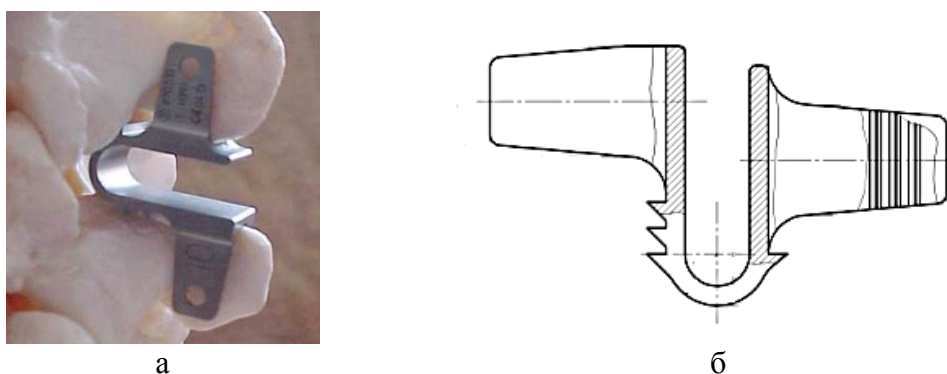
Имплантат, установленный в позвоночнике (а) [6] и чертеж детали «U-имплантат» (б)
